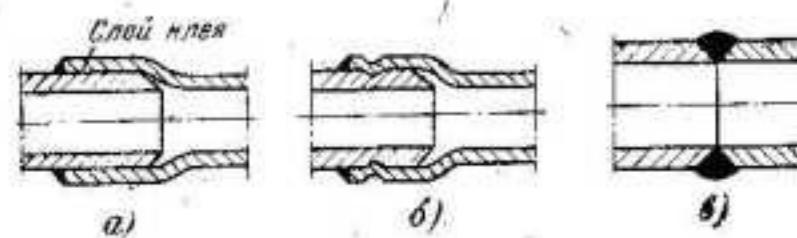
Типы соединений винилластовых труб на сварке.
